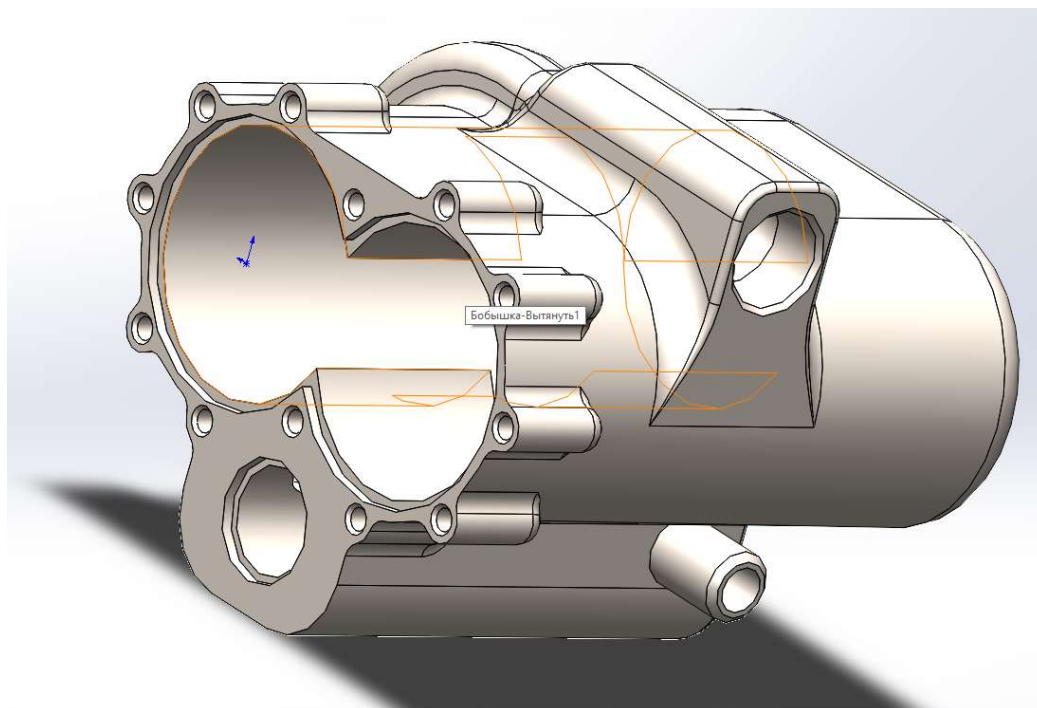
Трьох вимірна модель корпусу ізометричний вид
